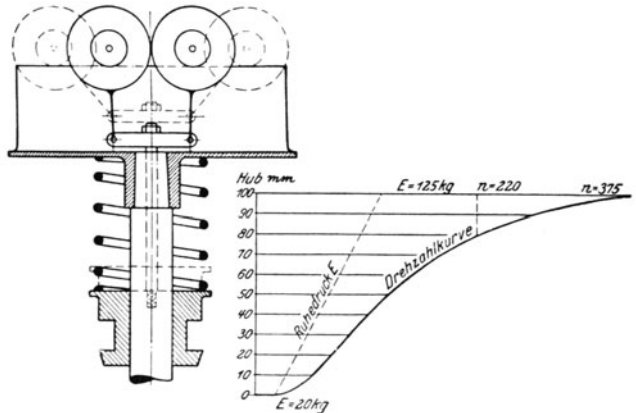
Fördermaschinenregler von Steinle & Hartung.
